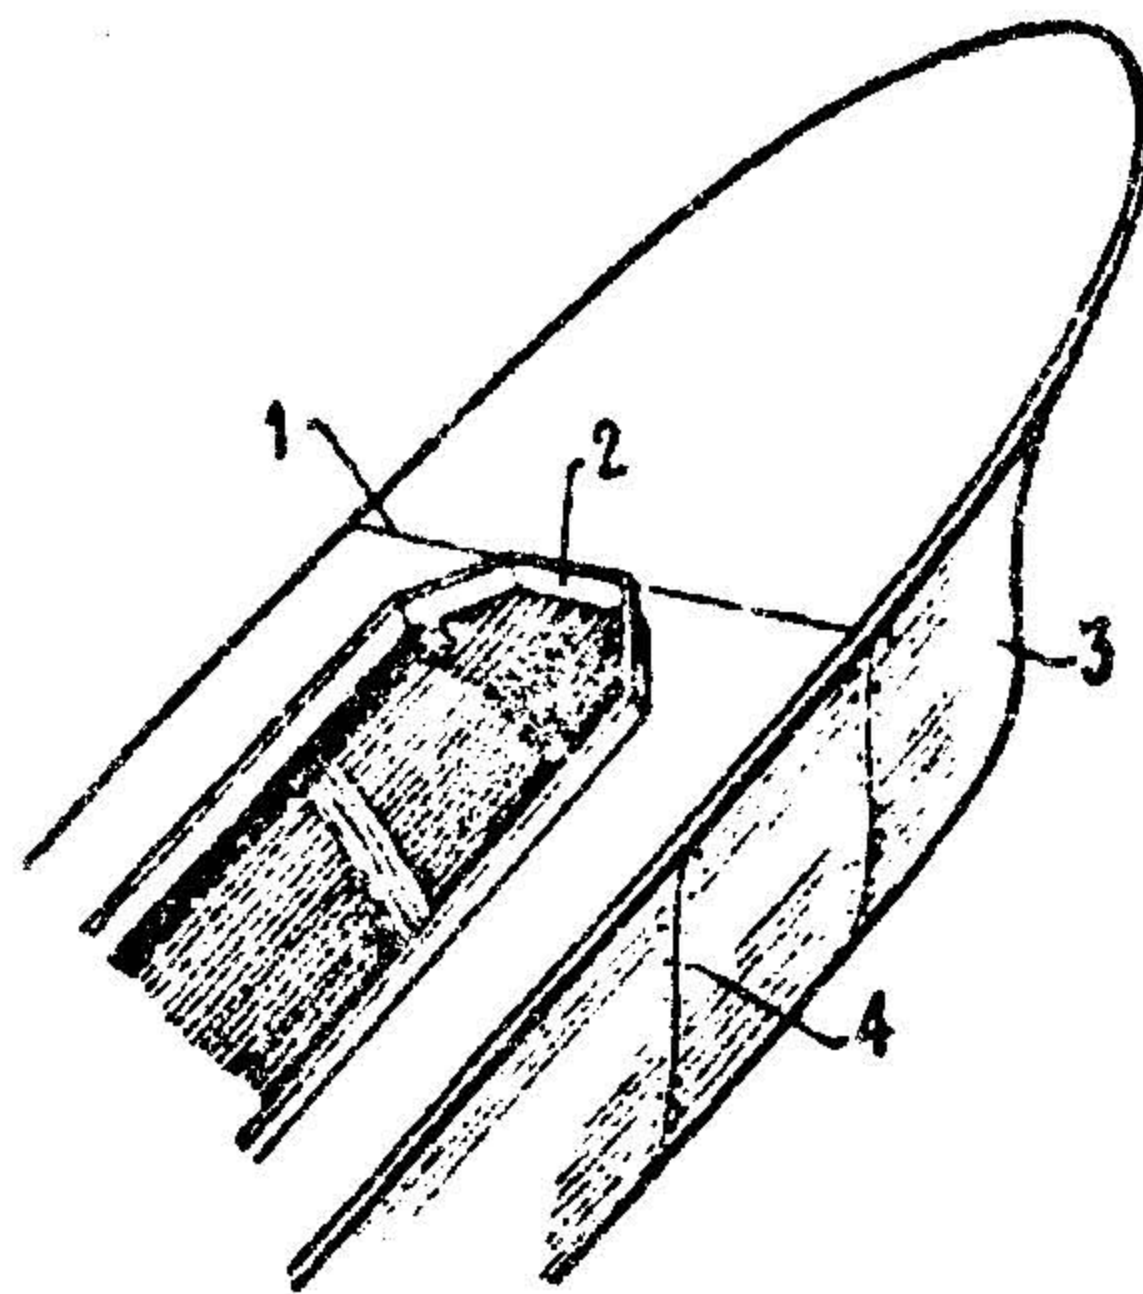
Установка комингса: 1 — стык на палубе; 2 — комингс; 3 — носовая часть корпуса; 4 — запаянные отверстия от гвоздей
